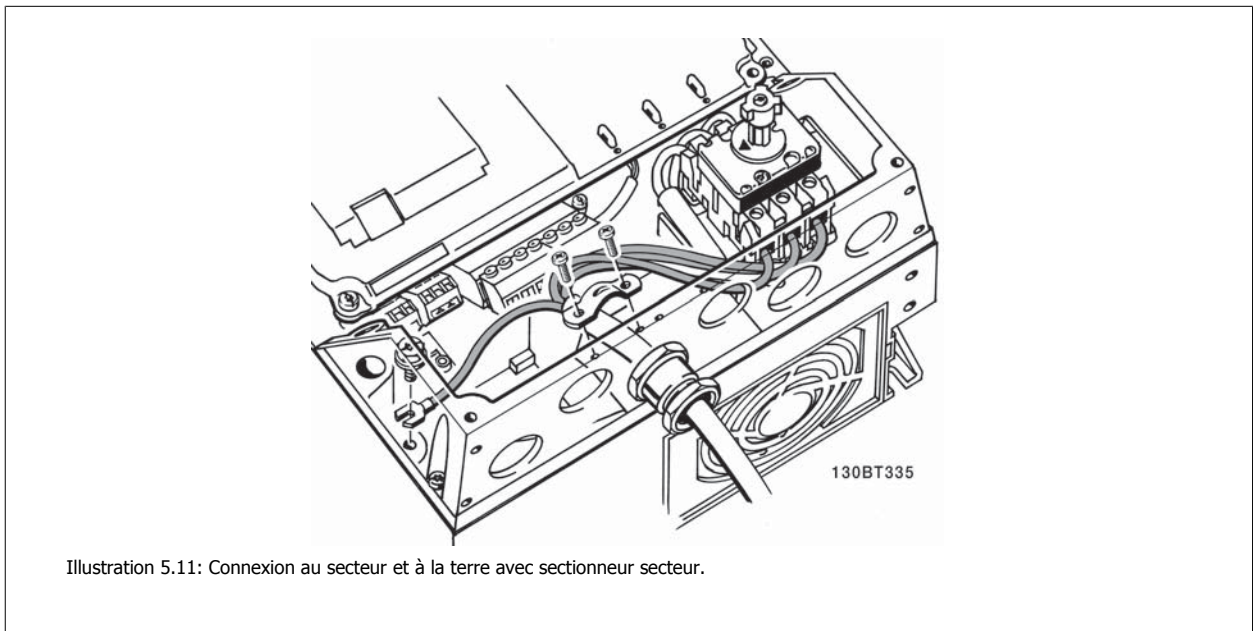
Connexion au secteur et à la terre avec sectionneur secteur.
